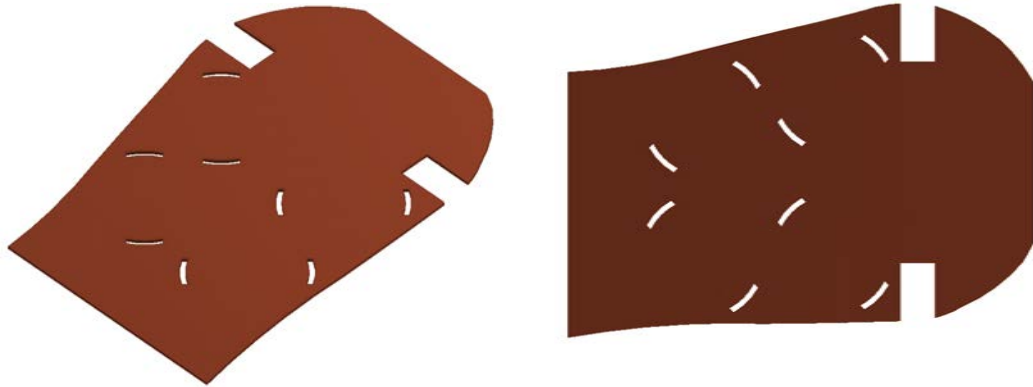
Forma del PCB. Fuente: Elaboración propia.
